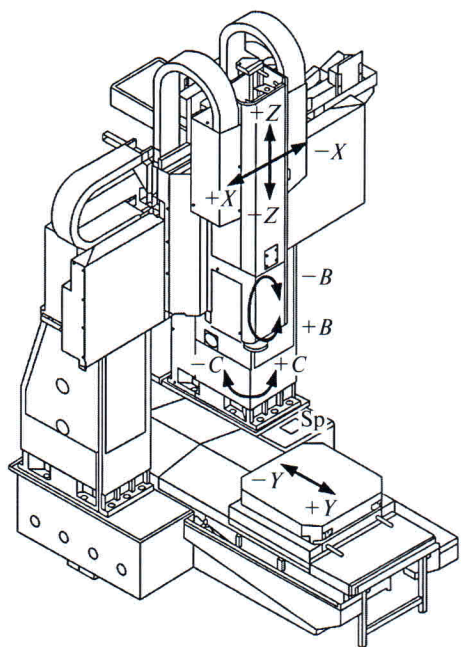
Кинематика строгально-фрезерного обрабатывающего центра мод. Э7106МФ4
